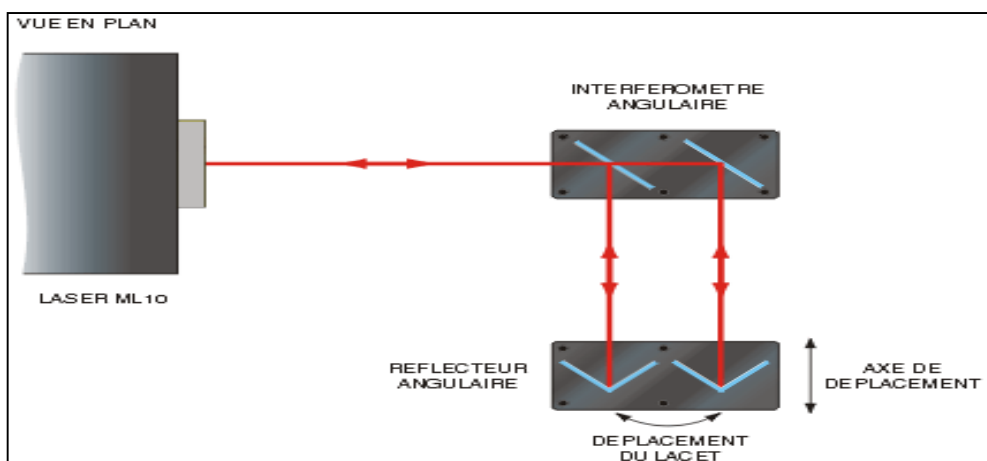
Mesure d'erreur de lacet - axe horizontal - à angle droit de la tête laser.
